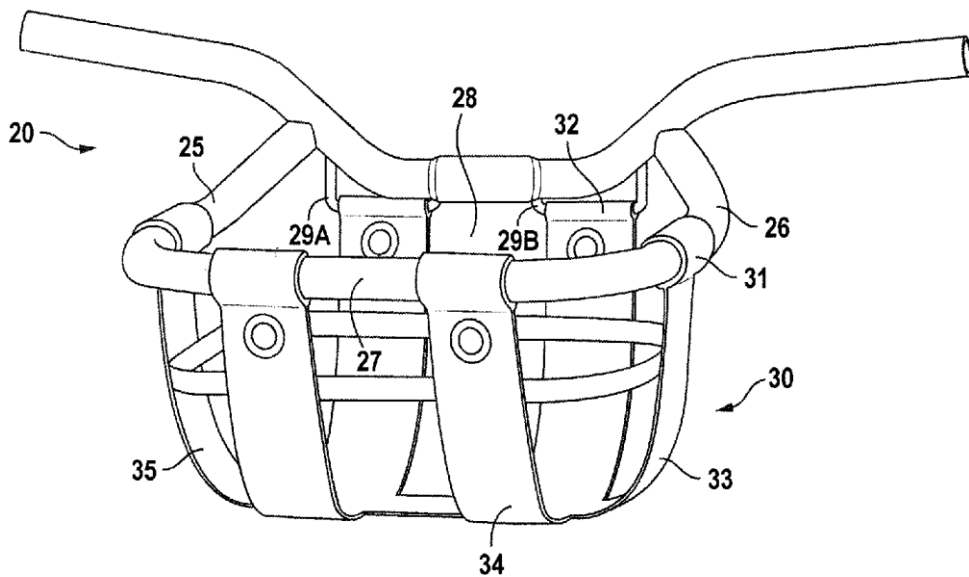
Patente para Canastilla Soldada al Manubrio (2012)
